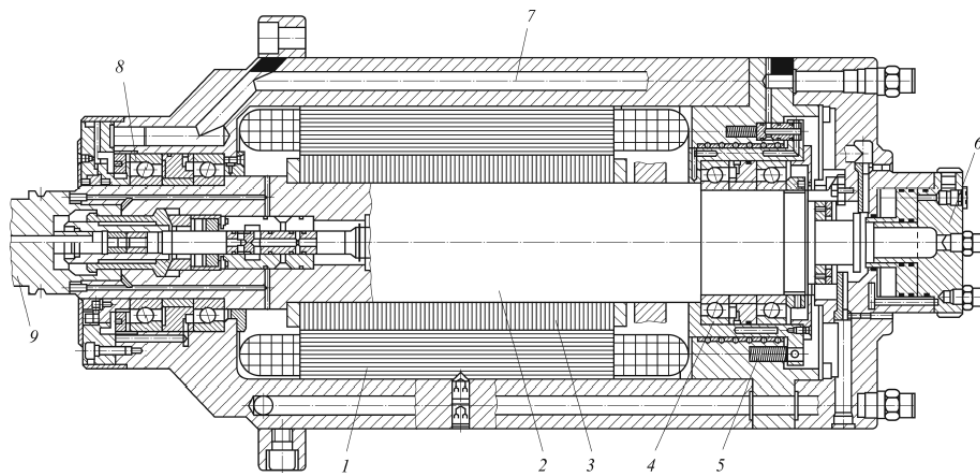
Загальна конструкція мотор-шпindelа: 1 – статор; 2 – шпindel; 3 – ротор; 4 – задня опора шпindelа; 5 – пружини для створення попереднього натягу; 6 – гідроциліндр; 7 – канали системи охолодження мотор-шпindelа; 8 – передня опора шпindelа; 9 – оправка
